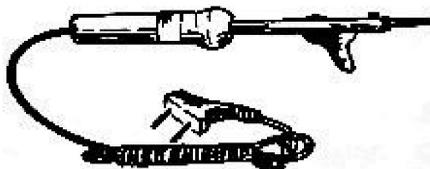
Ferro de soldar de pequena potência para a soldadura de semicondutores tipo transistores e circuitos integrados.
